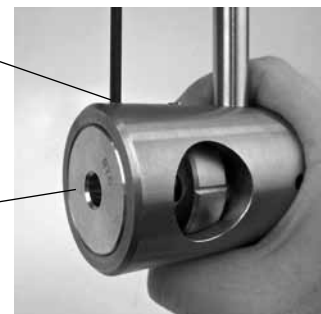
Gewindeschneidwerkzeughülse (Stirnfläche) und Sicherungsschrauben
